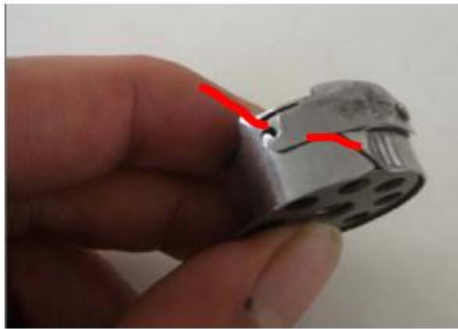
旋梭绕线 the rotary hook winds thread
